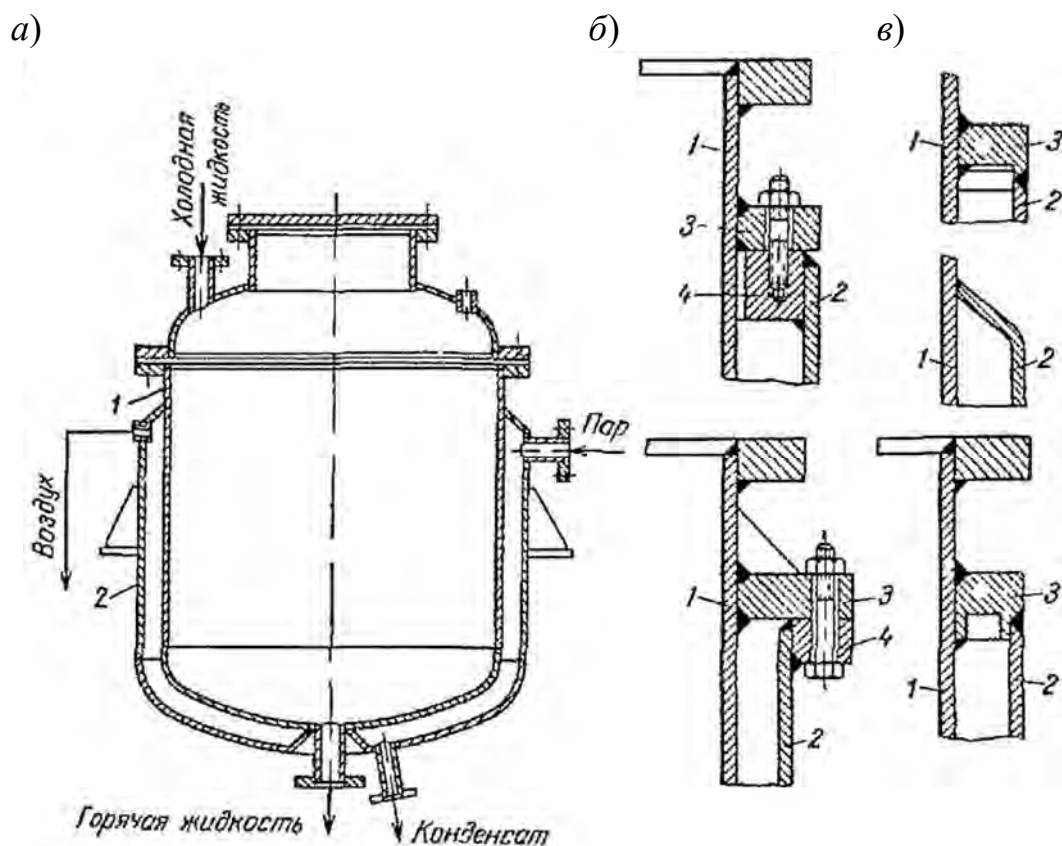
Аппарат с греющей рубашкой: а – аппарат с греющей рубашкой; б – фланцевый способ соединения рубашки; в – сварной способ соединения рубашки; 1 – корпуса сосудов; 2 – греющие рубашки; 3 – кольца; 4 – фланцы
